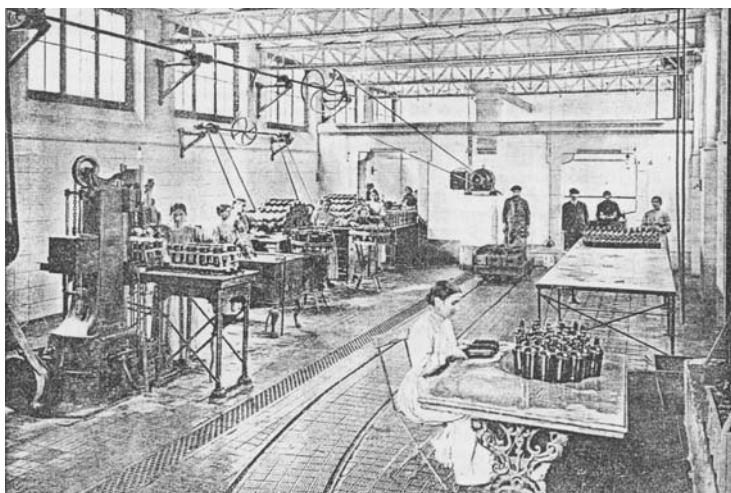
Piso inferior de la planta de embotellado: taller de lavado de botellas [Mondariz 1915 n° 3]
